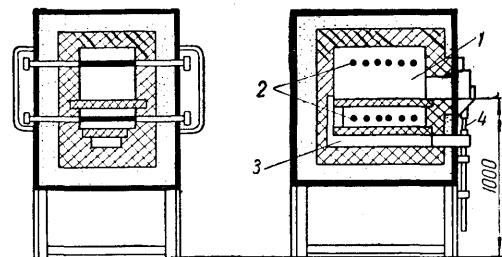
Электрическая печь с силитовыми нагревателями для нагрева стальных заготовок под ковку и штамповку в защитной атмосфере:
